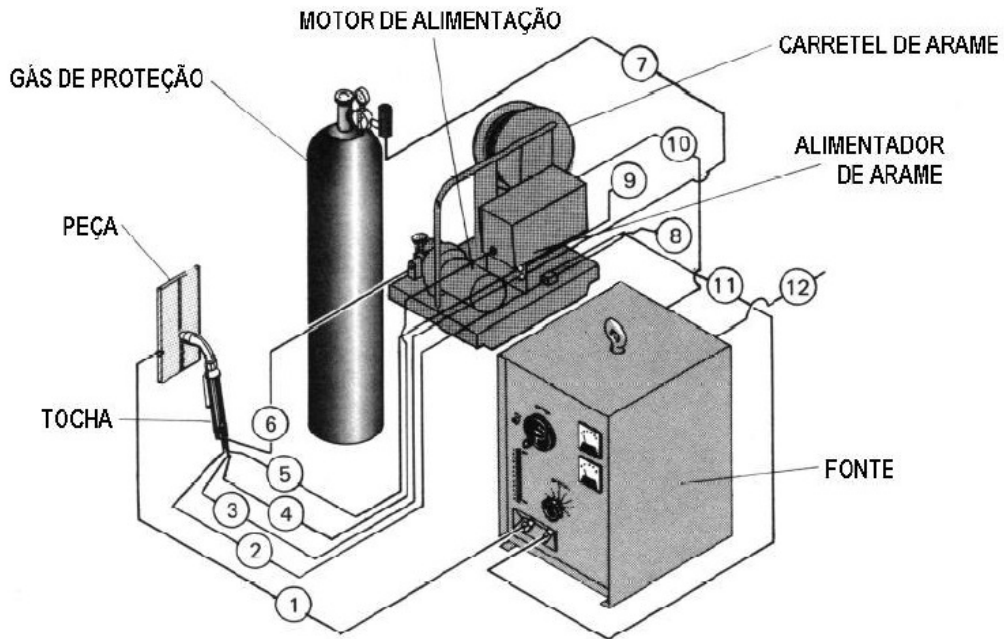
Equipamento básico de soldagem MIG / MAG (Esab, 2004)
